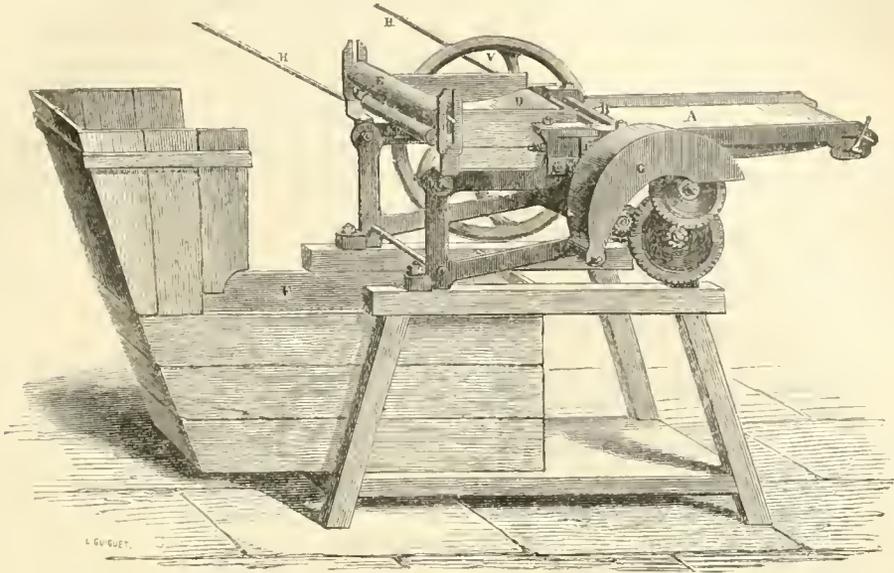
Vue de la deuxième machine à égrener le coton, de François Durand.
